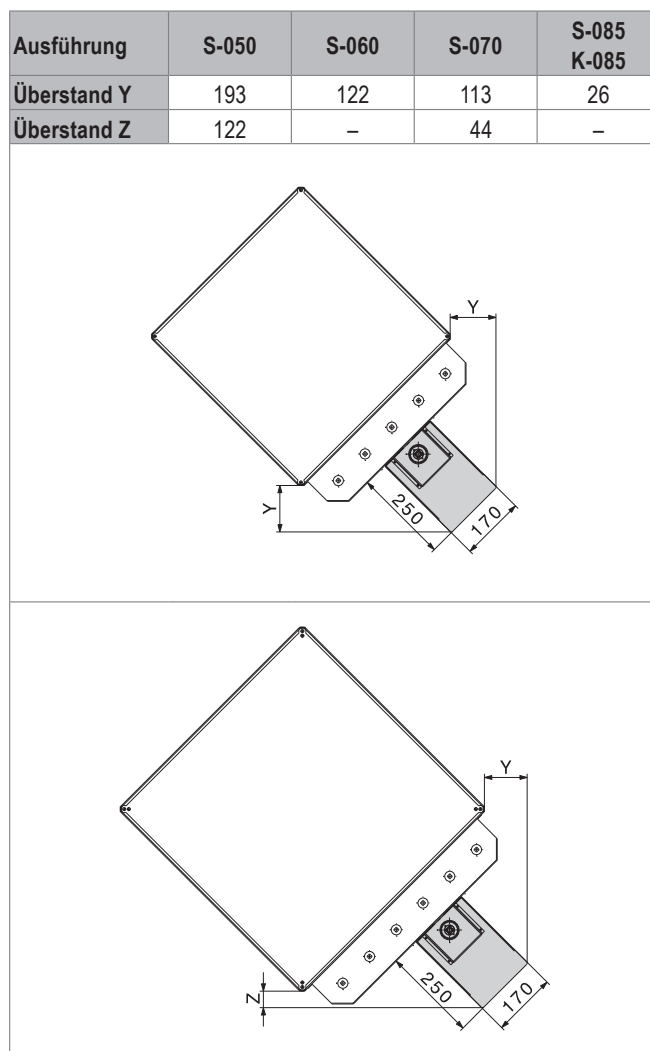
Massblatt Adapter für Krivan / Ausführung S (in mm)
